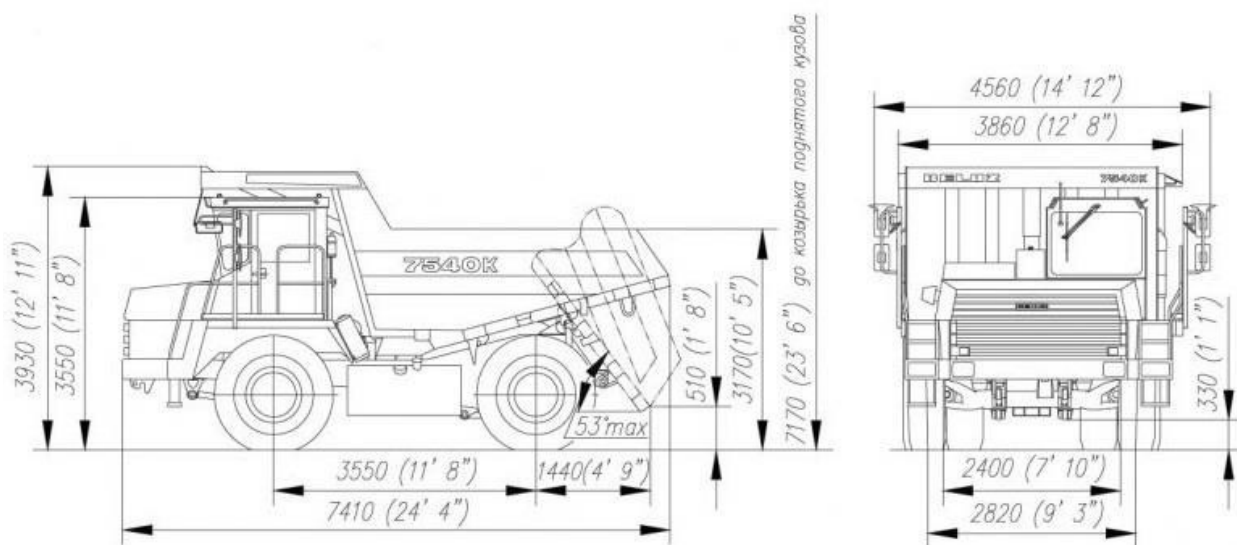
Габаритные размеры БелАЗ 7540А
